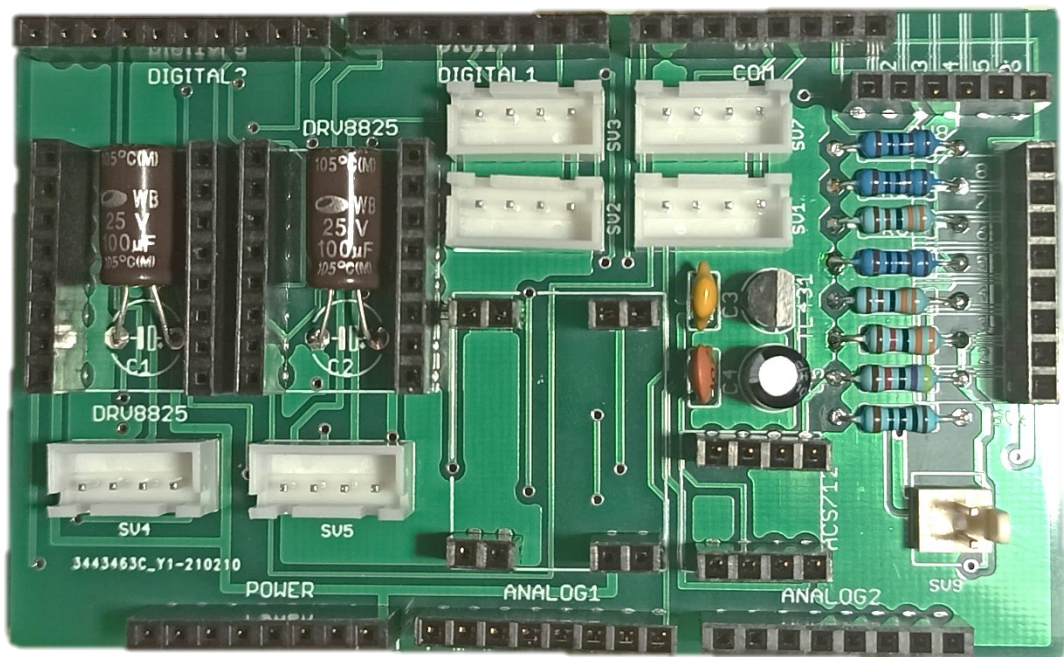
Rozmístění součástek desky plošných spojů
